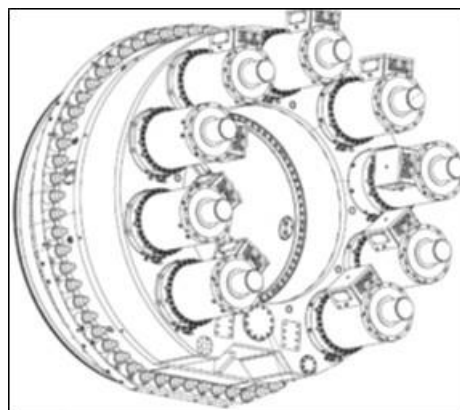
Accionamiento de cabeza de corte (Fuente: Expediente Técnico Final)
